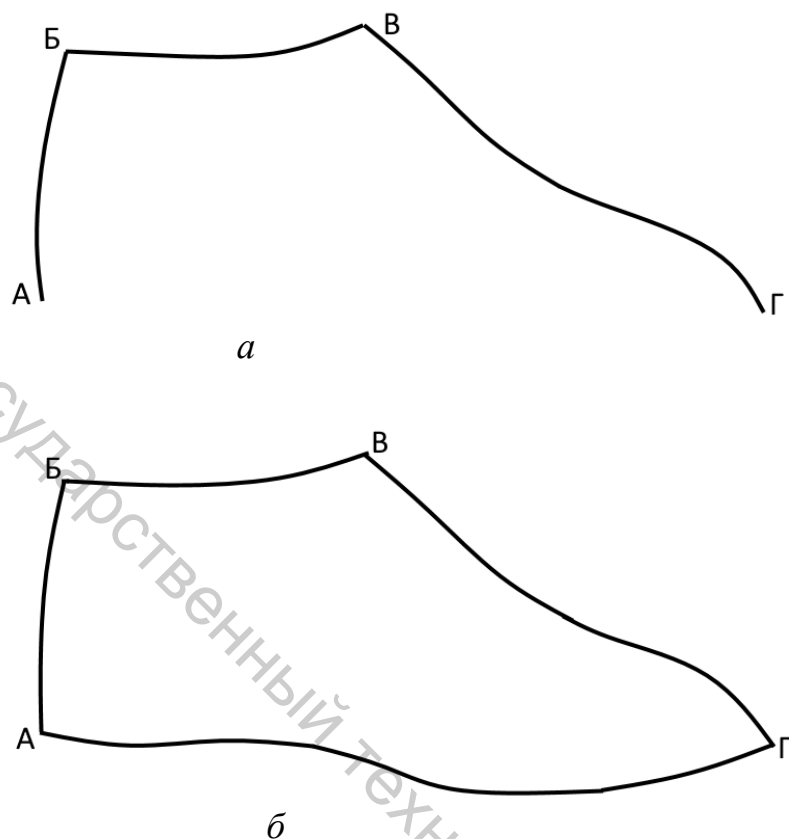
Распластывание условной развертки с внутренней боковой поверхности колодки
